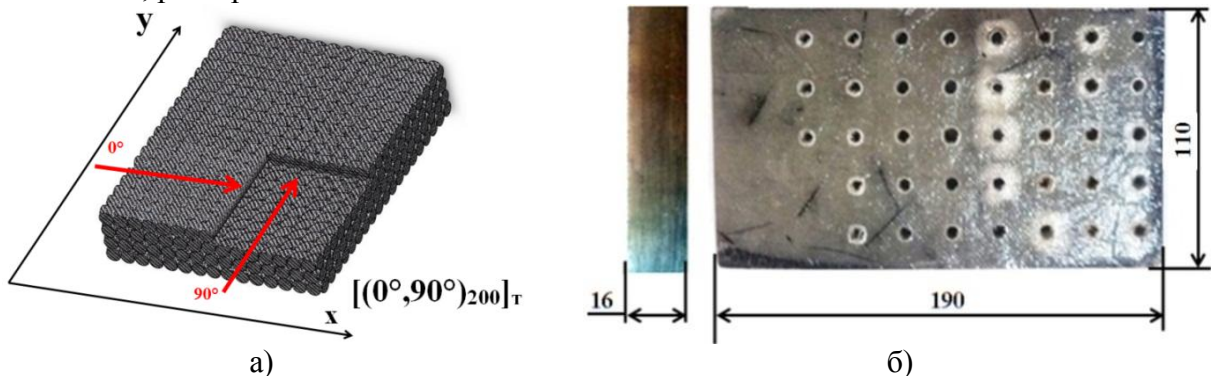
Склопластикова пластина з отворами із круглою внутрішньою різьбою, схема армування пластини а) фото пластини б).
